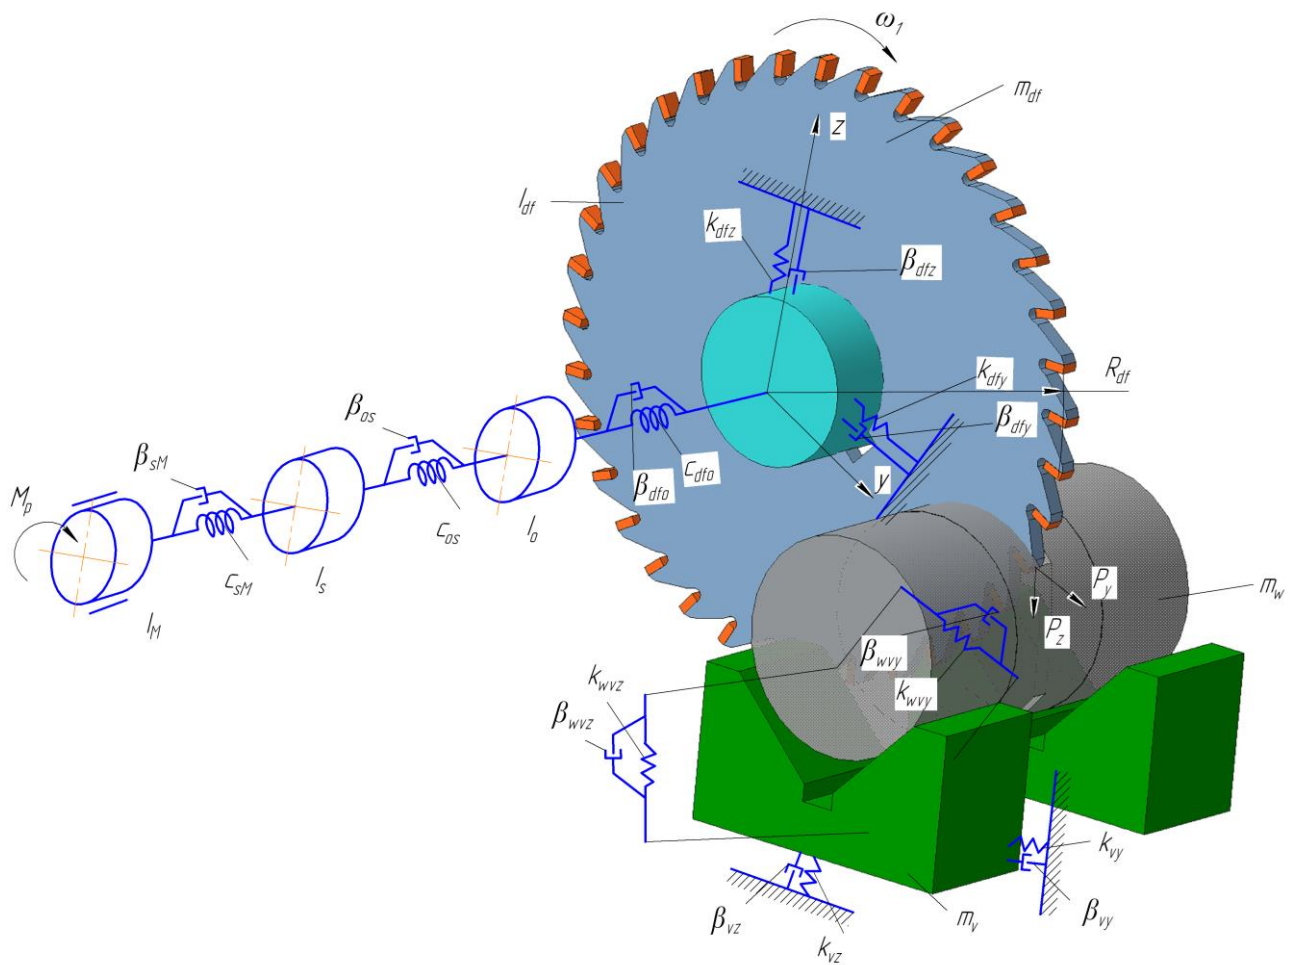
Схема динамічної моделі процесу різання циліндричної заготовки дисковою фрезою на фрезерно-відрізному верстаті
